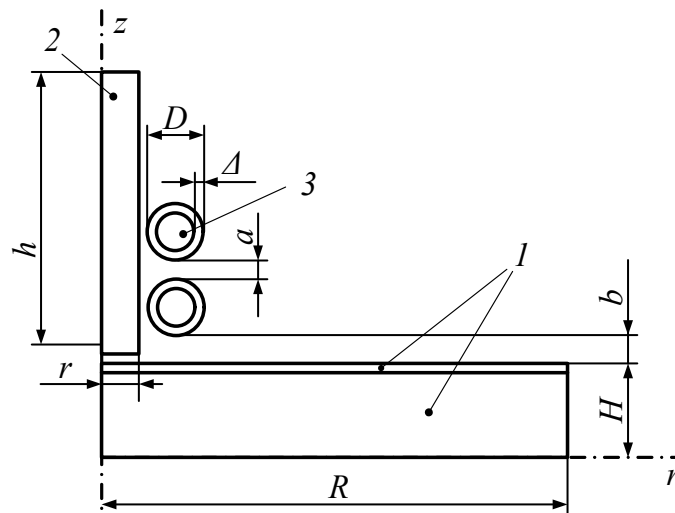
Геометрия модели индукционной точечной сварки: 1 – свариваемые части изделия; 2 – ферритовый стержень; 3 – индуктор
